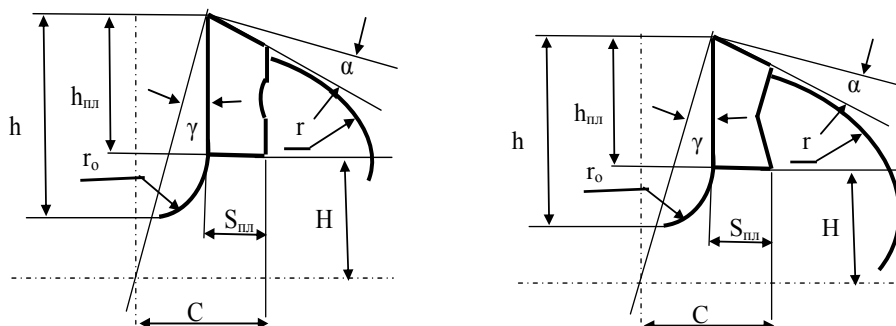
Профиль торцового сечения фрез с напайными пластинками для высокоскоростной обработки алюминиевых сплавов:
